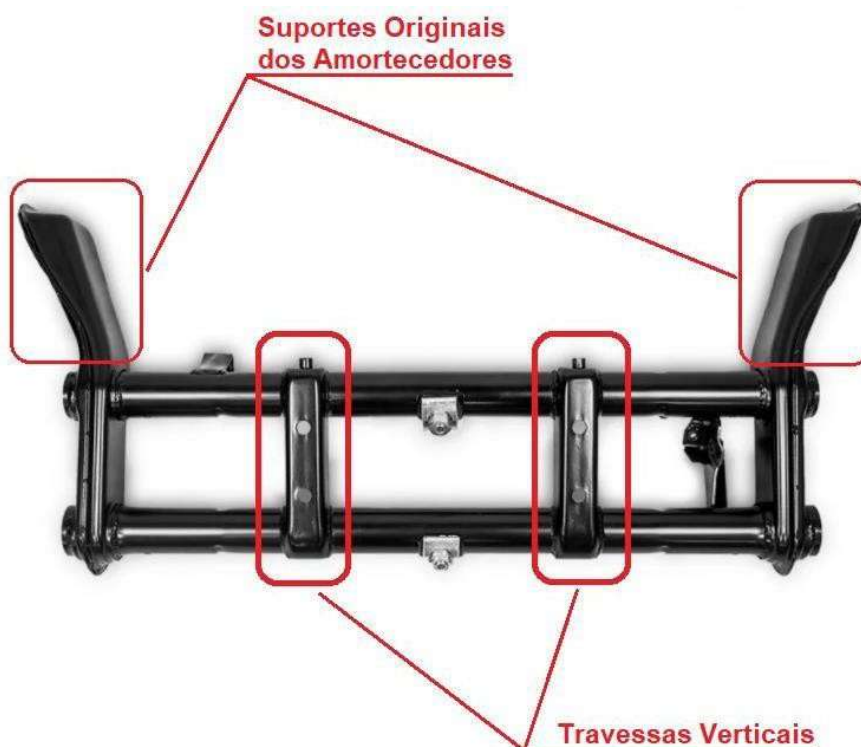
Identificação das travessas verticais e suportes originais dos amortecedores.
